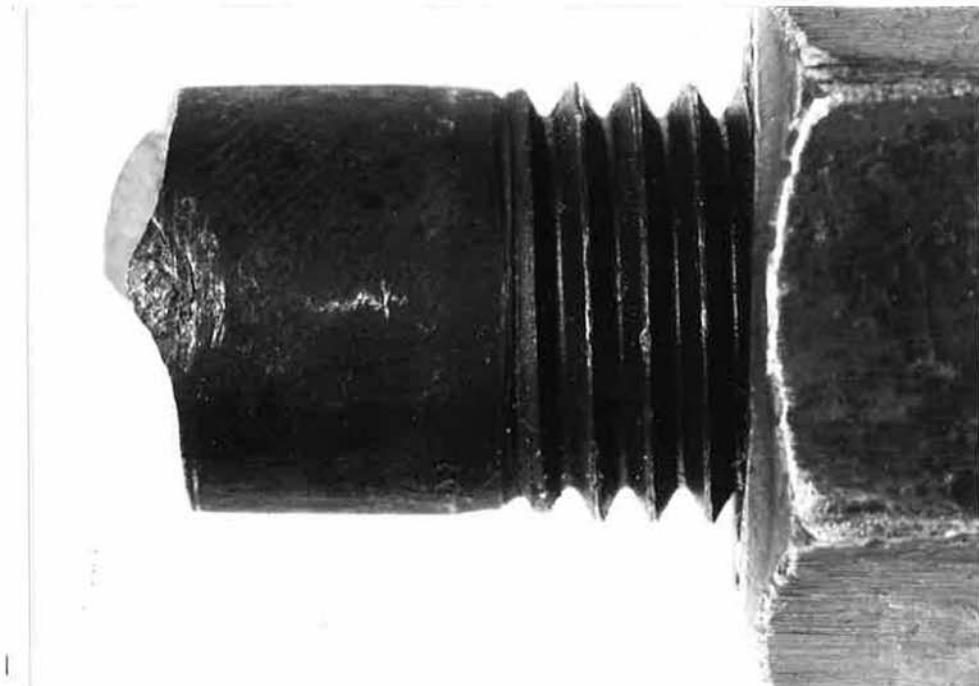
Reibkerben als Ursache für einen Dauerschwingriß am Schaft einer hochfesten Schraube M 16. Schraube a des Versuches Nr. T 23 (Versuchsreihe 8). Anrißstelle zugflanschseitig
